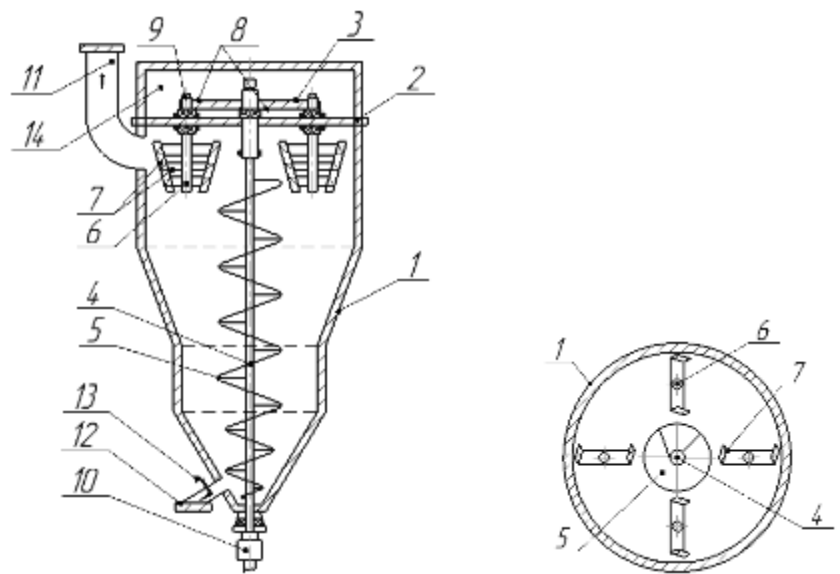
Змішувач кормів за патентом № 105446: 1 – змішувальна лійко-подібна камера; 2 – верхня кришка приводу; 3 – привідна шестерня; 4 – вал; 5 – вертикальний шнек; 6 – консольні вали; 7 – двоплощинні лопатки; 8 – консольні вали; 9 – привідні шестерні; 10 – електродвигун; 11 – завантажувальна горловина; 12 – вивантажувальна горловина; 13 – заслінка; 14 – захисний кожух
